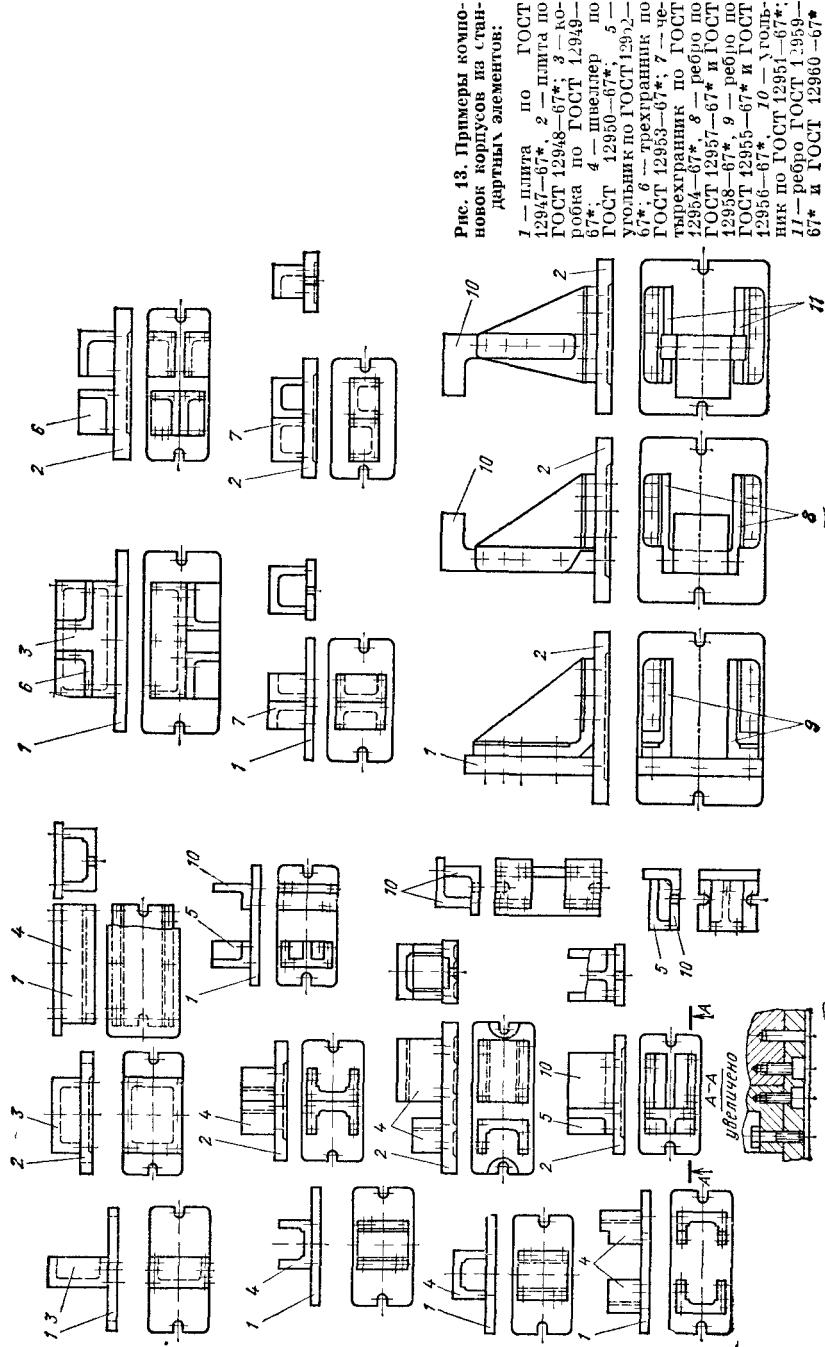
Примеры комбинировок корпусов из стандартных элементов:
